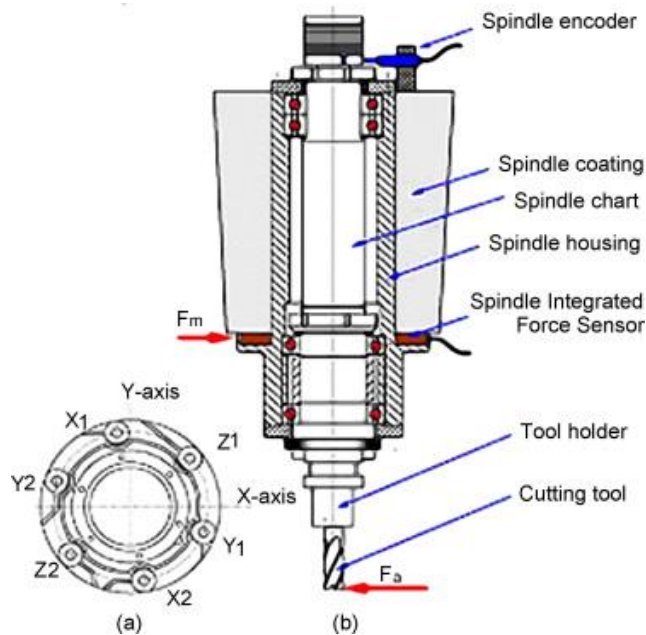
Integrierte Kraftsensoren in der Motorspindel²⁹
